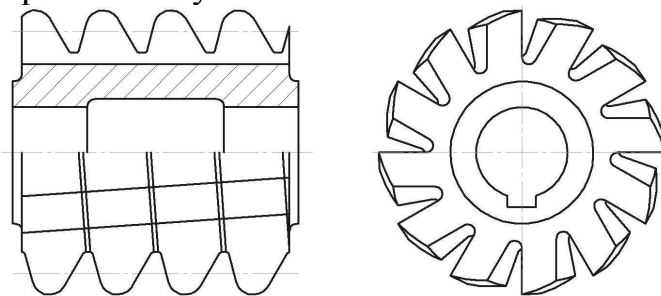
Общий вид червячной фрезы для нарезания звездочек с несимметричными зубьями
